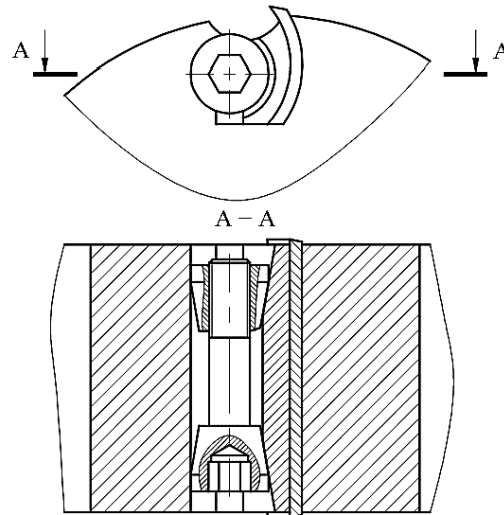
Узел крепления режущего ножа с осевым расположением винта
